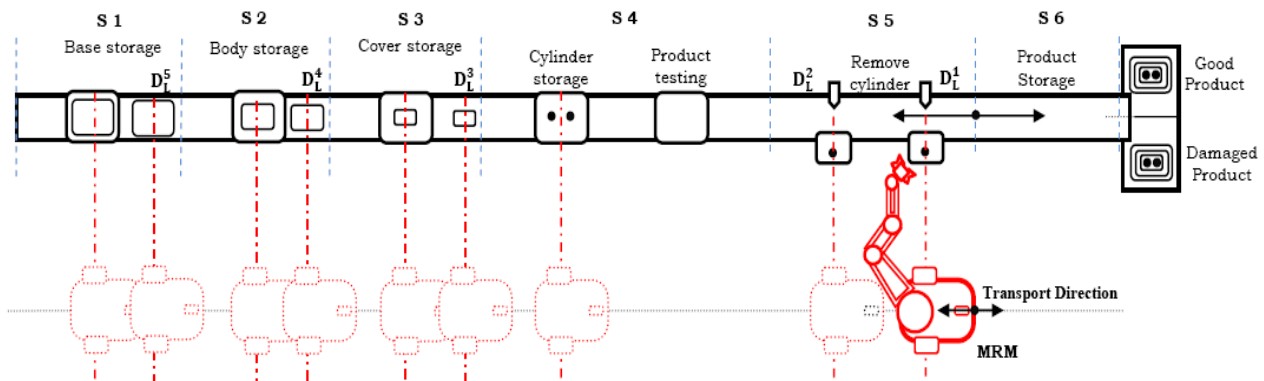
Linia mecatronică de asamblare/dezasamblare a unei piese cu 5 componente, deservită de un robot mobil echipat cu manipulator.
